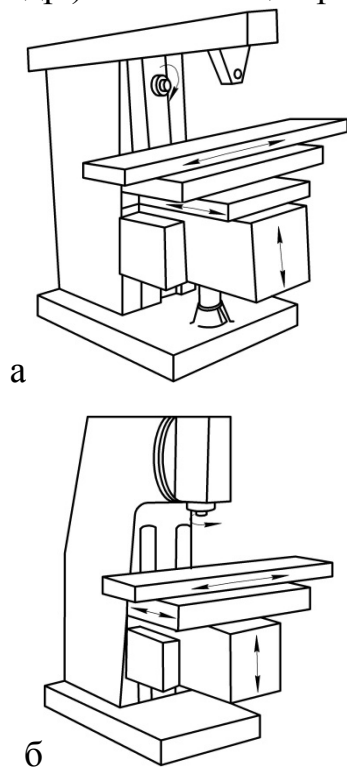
Компоновка консольных горизонтально-фрезерного (а) и вертикально-фрезерного (б) станков
